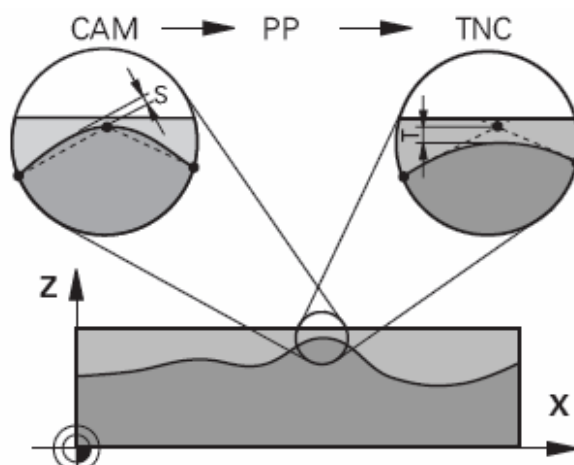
Tolerance v cyklu 32⁴.
